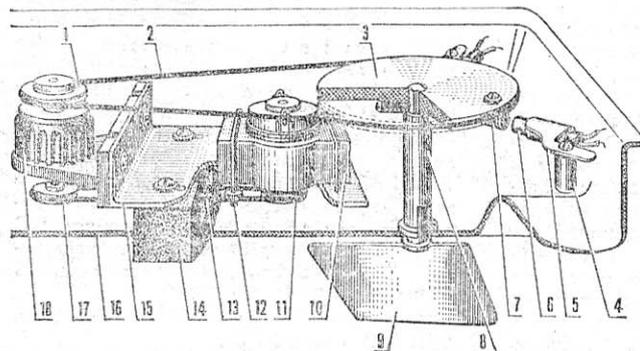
Машинка привода руля: 1 — верхний шкив редуктора, 2, 13 — резиновые кольца, 3 — шкив руля, 4 — втулка, 5 — скоба, 6 — геркон, 7 — магнит, 8 — втулка оси руля, 9 — перо руля, 10 — электродвигатель, 11 — шкив электродвигателя, 12 — скоба, 14 — подставка, 15 — угольник, 16 — корпус судна, 17 — нижний шкив редуктора, 18 — редуктор.
